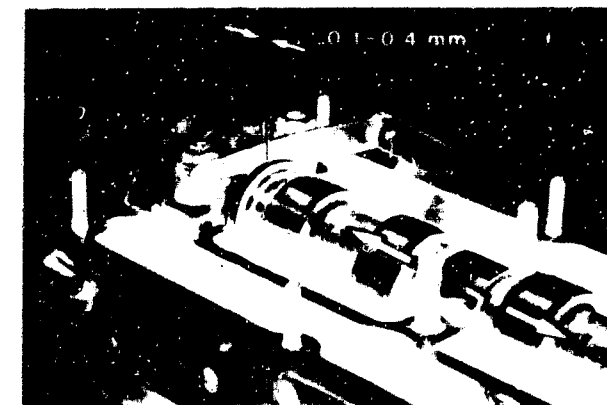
Motoren B 200, B 230: Messen des Axialspiels bei aufgesetztem hinterem Lagerdeckel durch Hin- und Herschieben der Nockenwelle.
